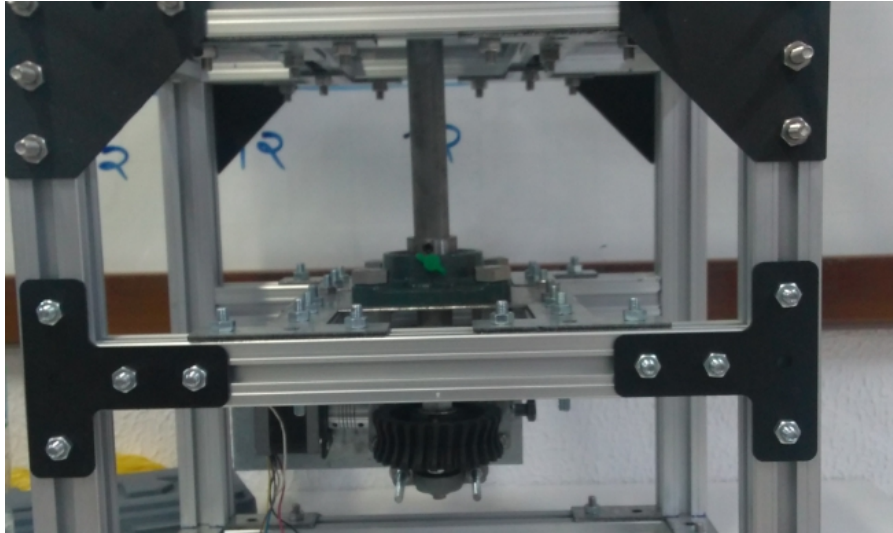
Eixo horizontal acoplado com redução e motor de passo.
